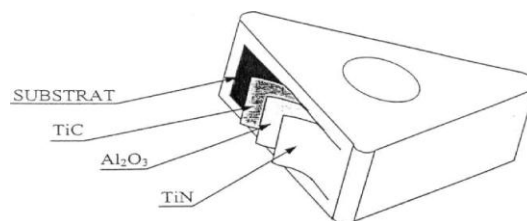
Plaquette carbure revêtue, multicouches [6]
